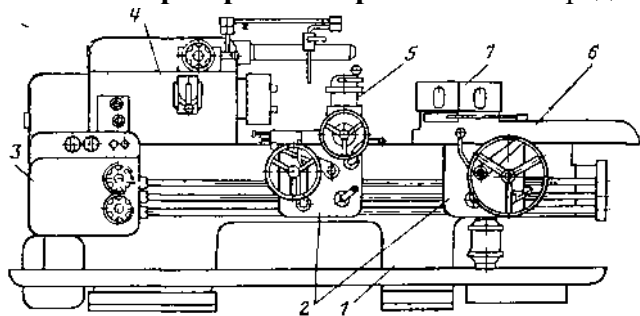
Общий вид токарно-револьверного станка модели 11365.
